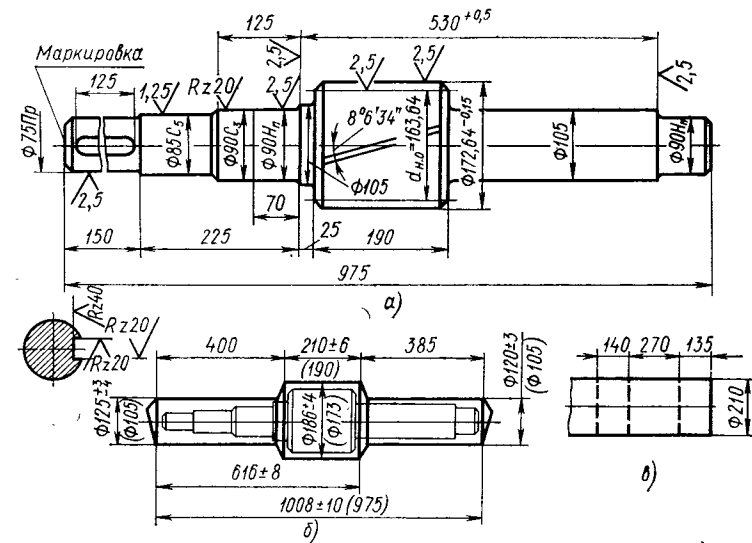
Вал-шестерня (а), поковка (б) и эскиз переходовковки (в)
